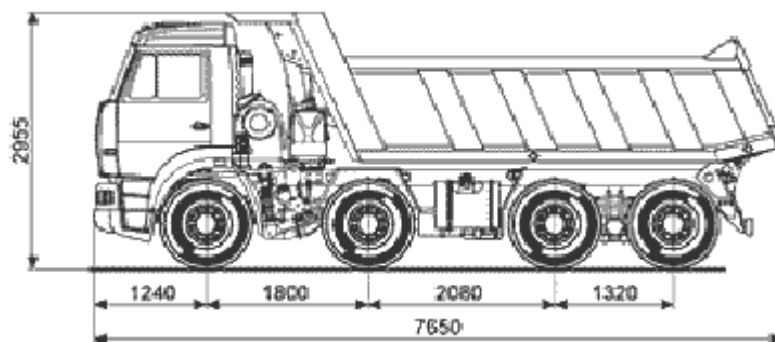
Габаритные размеры самосвала КамАЗ – 6540
